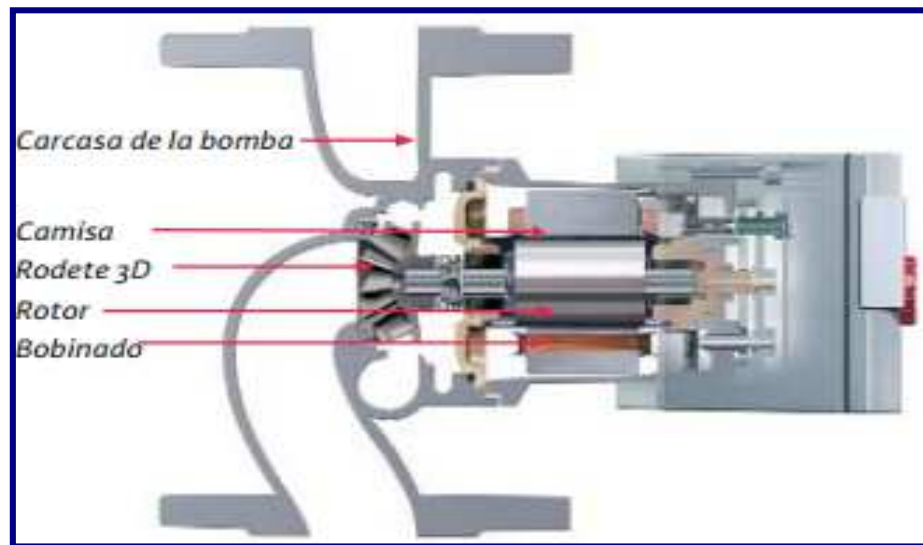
Partes principales de una bomba de rotor húmedo (www.wilo.es)
